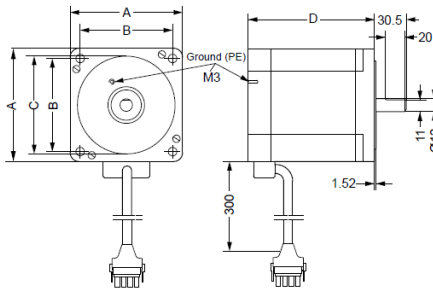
Размеры шагового двигателя для диапазона 1-8 Нм
